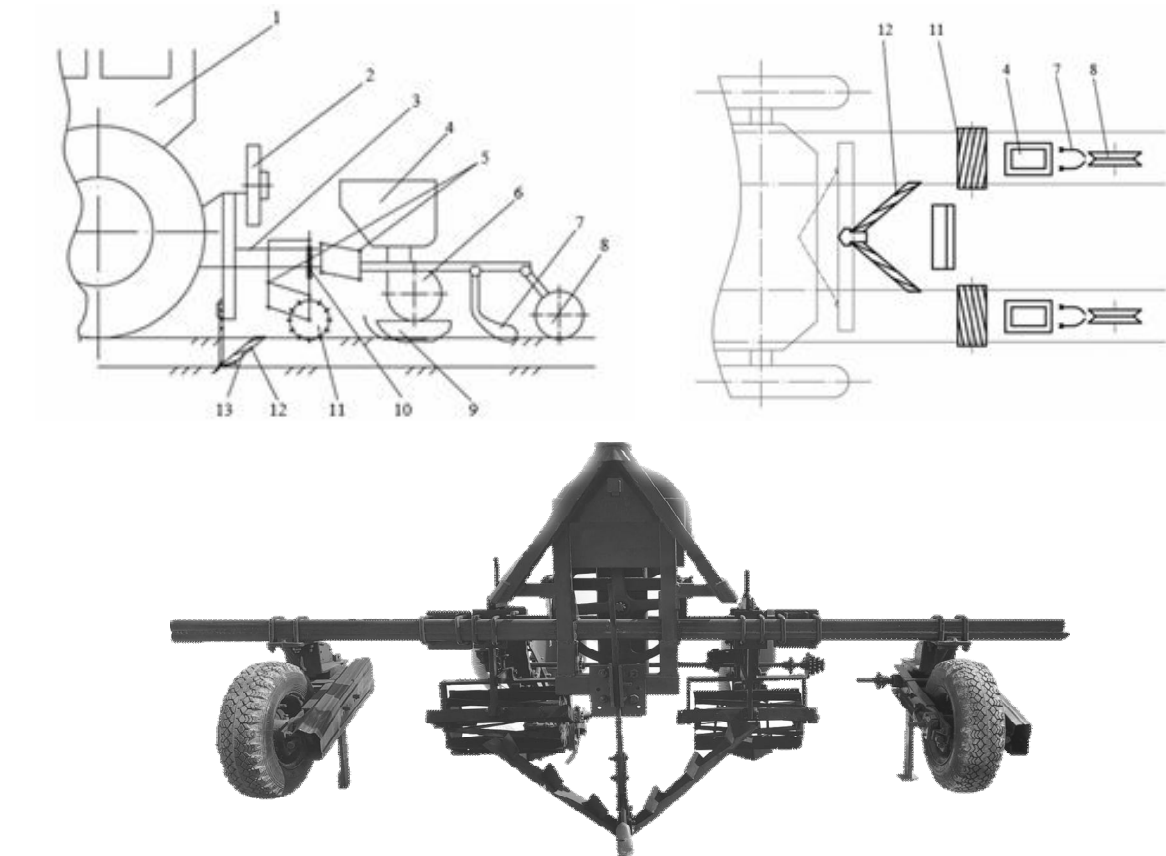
Конструктивная схема и общий вид комбинированного агрегата: 1 – трактор; 2 – эксгаустер; 3 – рама; 4 – бункер; 5 – параллелограммный механизм; 6 – пневматический высевающий аппарат; 7 – загортач; 8 – прикатка; 9 – полозовидный сошник; 10 – пружина; 11 – ротационный рыхлитель; 12 – нож; 13 – почвосдвигающая пластина.
